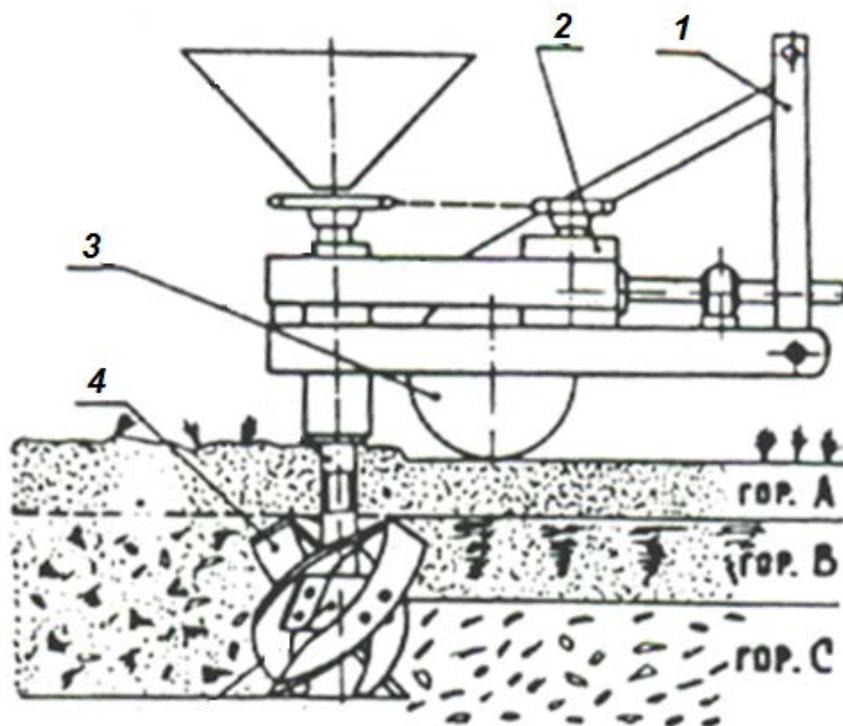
Подпокровный фрезерователь с вертикальной осью вращения: 1-балка крепления, 2-привод, 3-опорный ролик, 4-фреза
